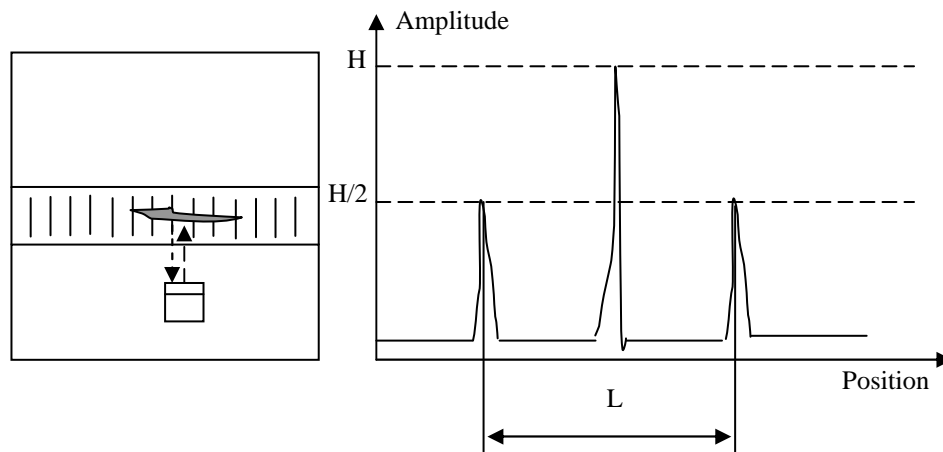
Dimensionnement d'un défaut par la méthode –
